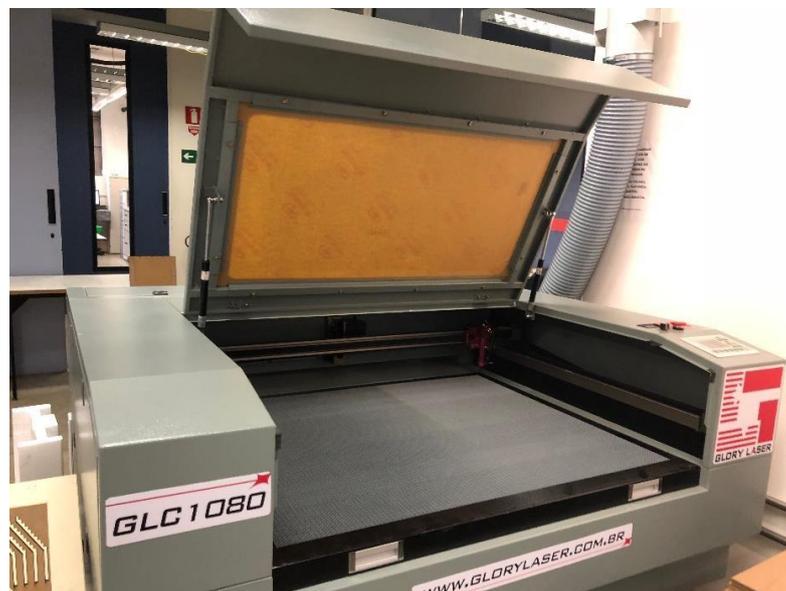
Máquina de corte à laser Glorylaser GLC 1080.
